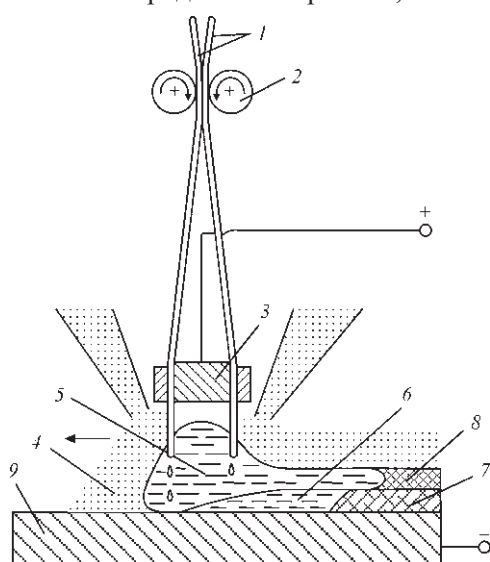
Схема электрошлаковой наплавки двумя лентами [4]: 1 — электродные ленты; 2 — подающие ролики; 3 — медная вставка; 4 — шлак (флюс); 5 — шлаковая ванна; 6 — металлическая ванна; 7 — наплавленный металл; 8 — шлаковая корка; 9 — заготовка
